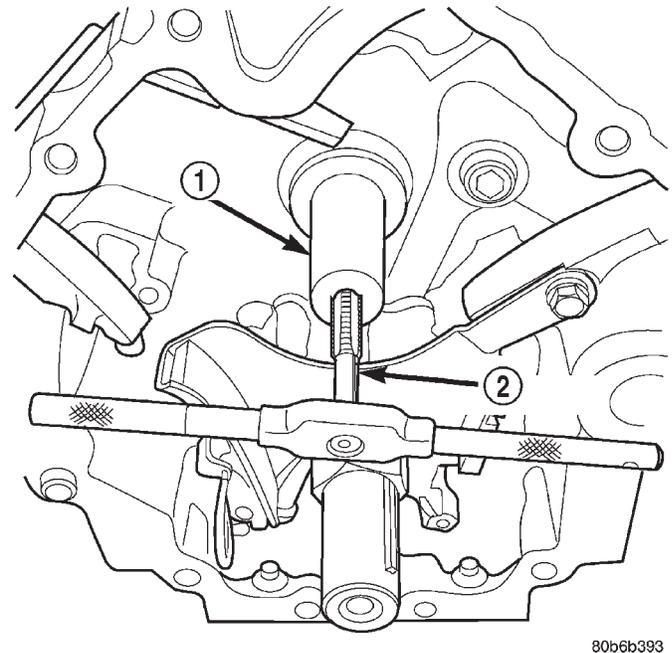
Zwischenwelle zur Aufnahme von Spezialwerkzeug 8517 mit einem Gewinde versehen
